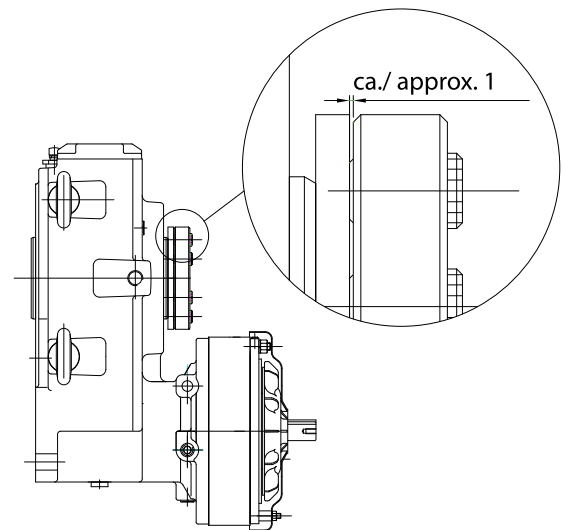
Einstellen des Spalts zwischen Taper Grip Flansch und Druckring
